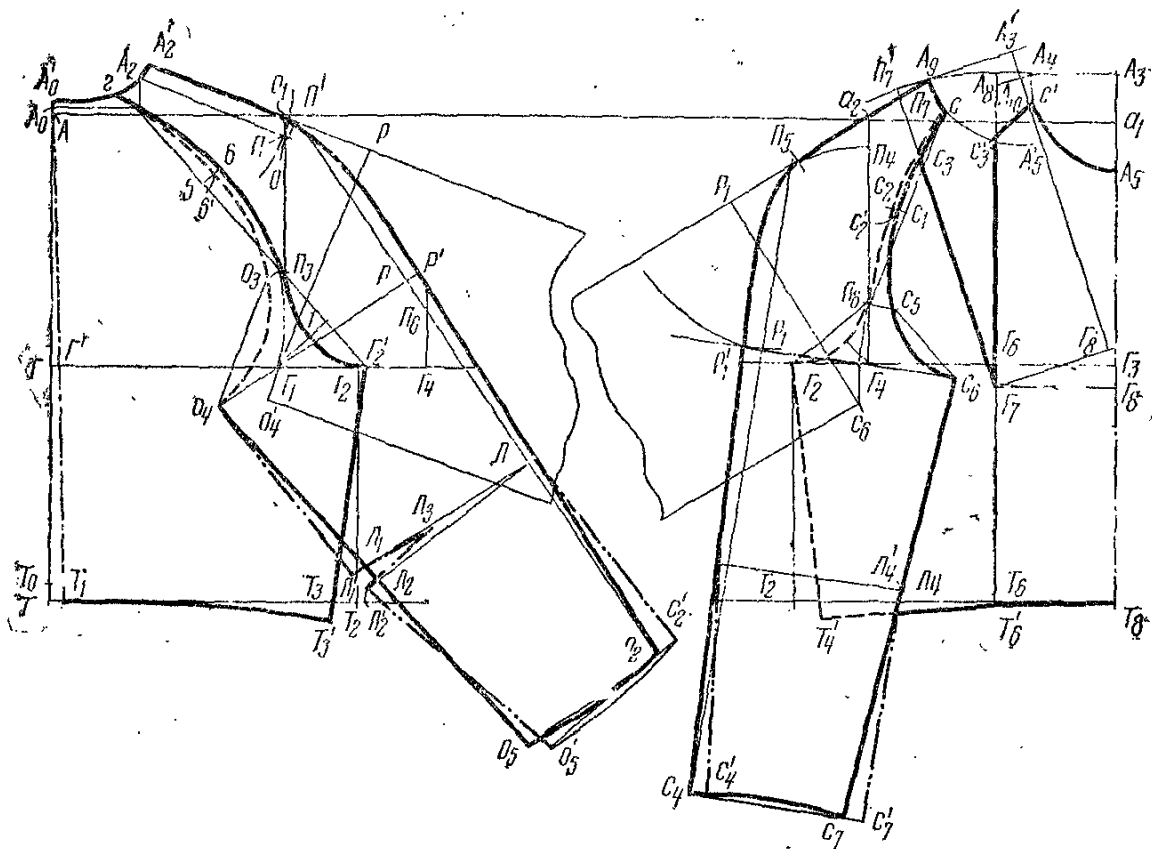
Чертеж лифа платья с рукавами покрой реглан
